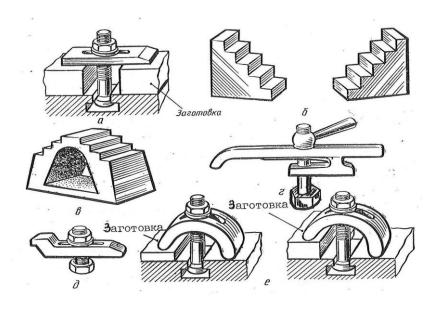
Универсальные станочные приспособления – прихваты
